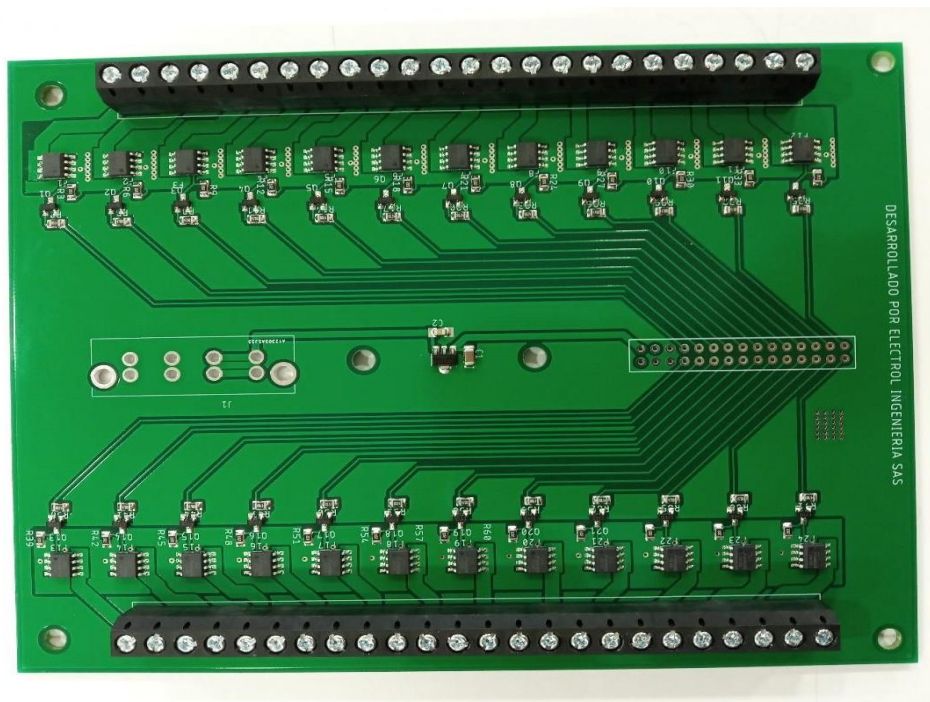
Tarjeta DC PCB secuenciador de luces con sus componentes. Tobón. (2019)
